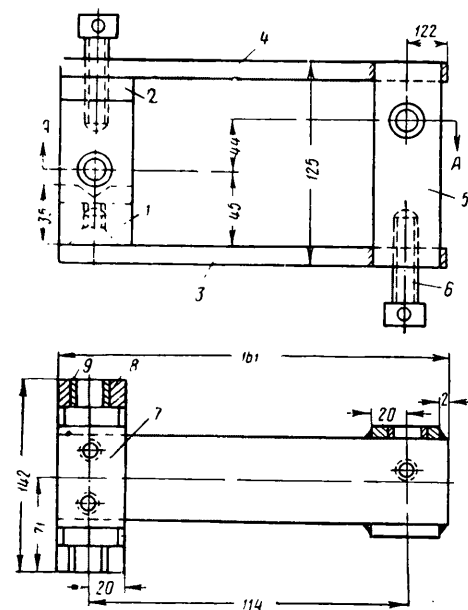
Кондуктор для сверления отверстий под валик в рычаге полоза:
